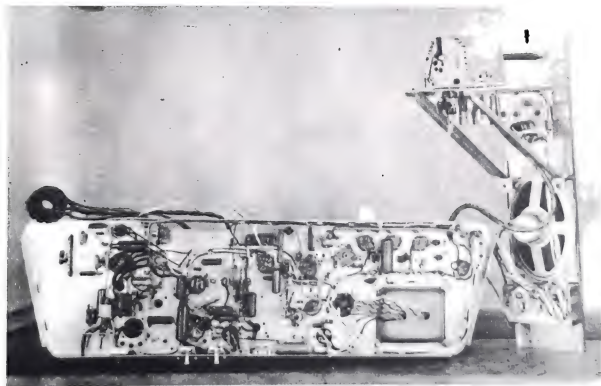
En esta foto se ha terminado la conexión de elementos y se han conectado además los cables que unen los dos chasis
